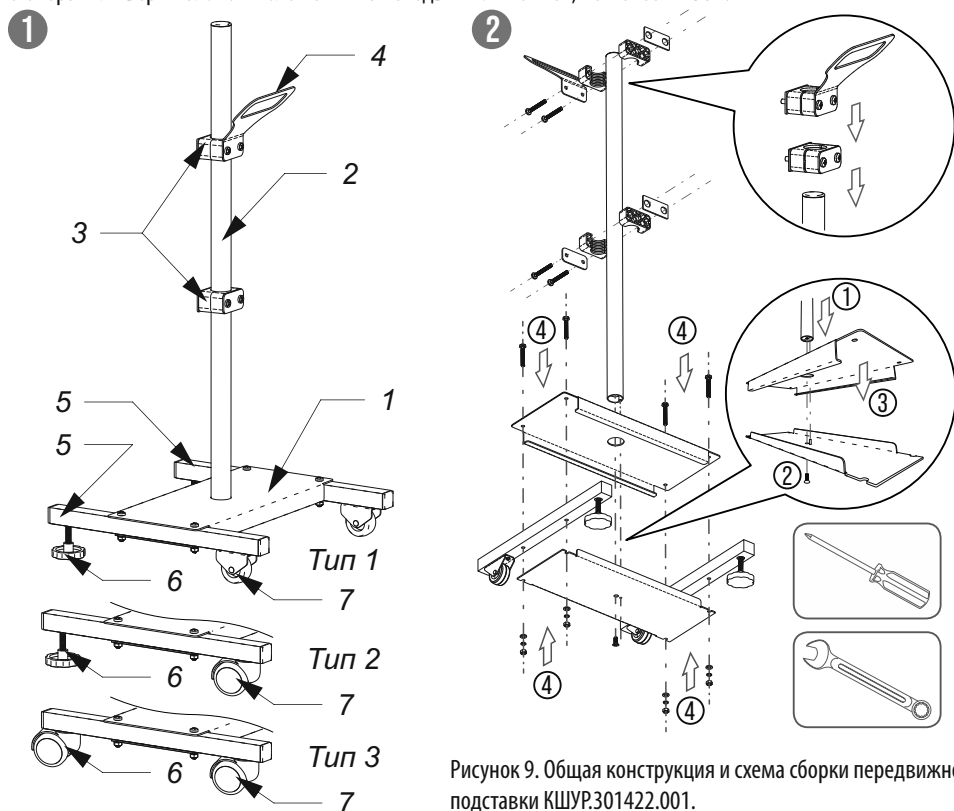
Общая конструкция и схема сборки передвижной подставки КШУР.301422.001.
